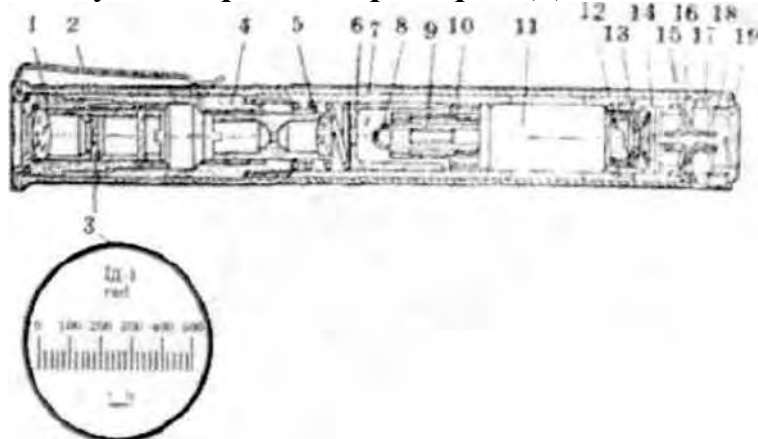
Будова дозиметра ІД-1: 1 - окуляр; 2 - пружина; 3 - тримач; 4 - об'єктив; 5 - пружина; 6 - електрод зовнішній; 7 - корпус; 8 - електрод внутрішній; 9 - пружина; 10 - електрод центральний; 11 - конденсатор; 12 - вивід; 13 - обмежувач; 14 - контакт; 15 - діафрагма; 16 - кільце; 17 - гайка; 18 - захисний ковпачок; 19 - ковпачок зарядного гнізда
